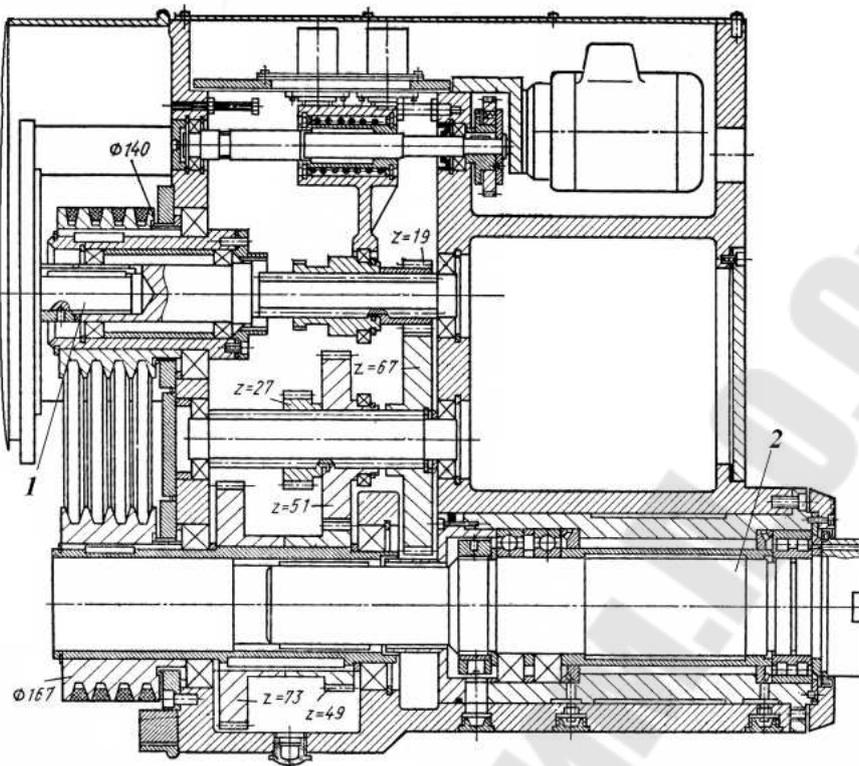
Шпиндельная бабка фрезерно-сверлильного многооперационного станка:
